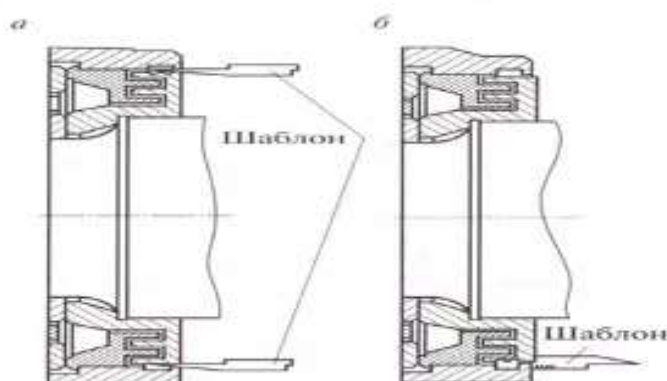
Схема проверки зазоров лабиринтным кольцом и корпусом буксы (а) и схема проверки смещения корпуса буксы относительно лабиринтного кольца (б)
